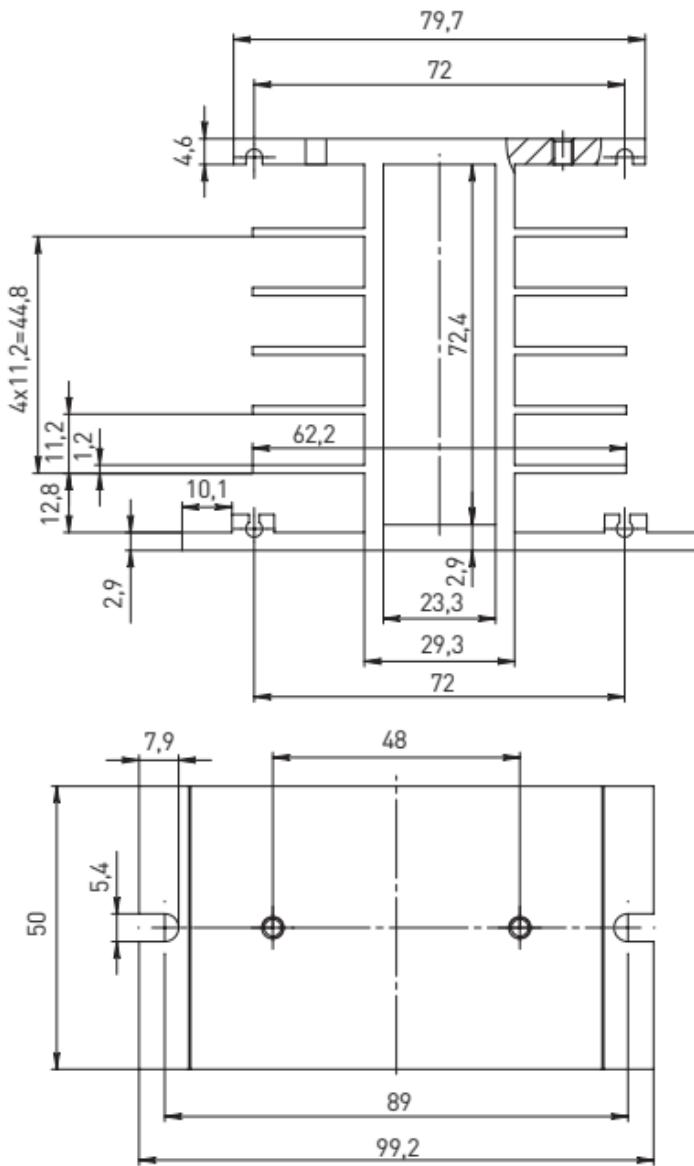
Габаритные размеры радиатора для твердотельного реле 60А
